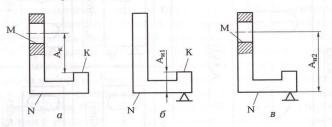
Выбор установочной базы: a — чертеж конструктора; b — операция № 1; b — операция № 2
